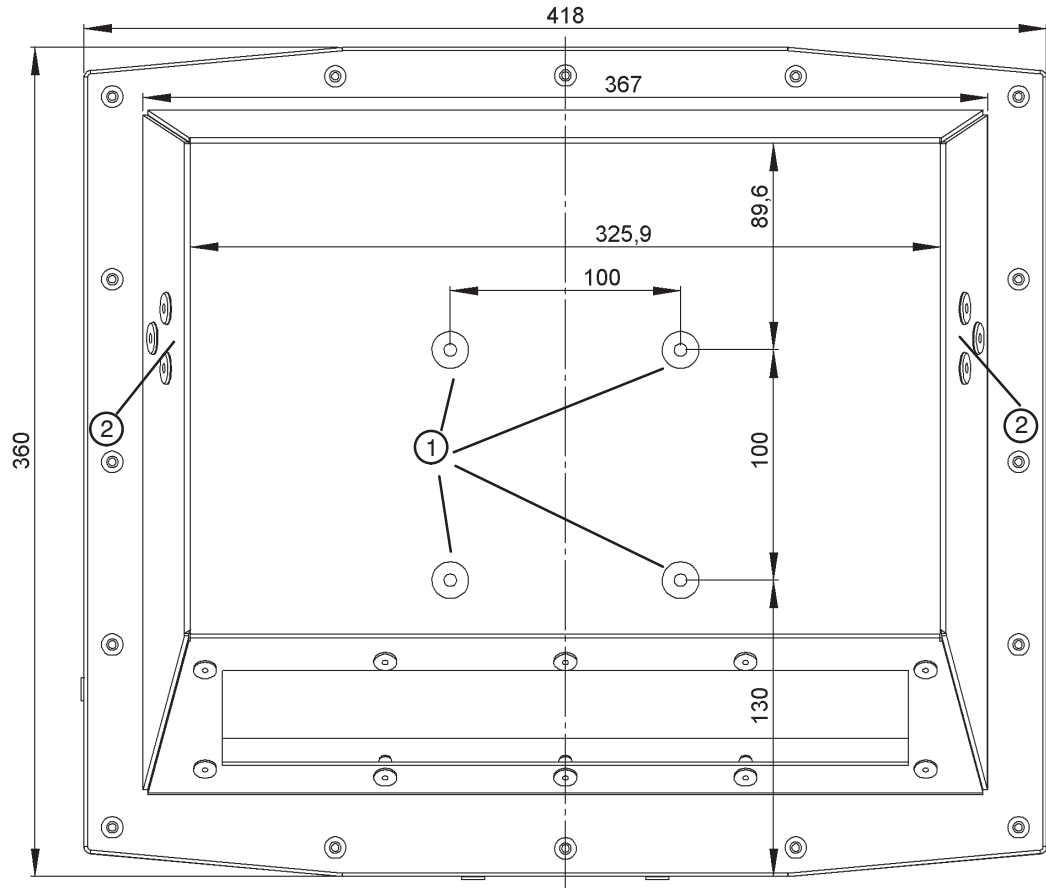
Rückwand S15-G2 (alle Maße in mm)
